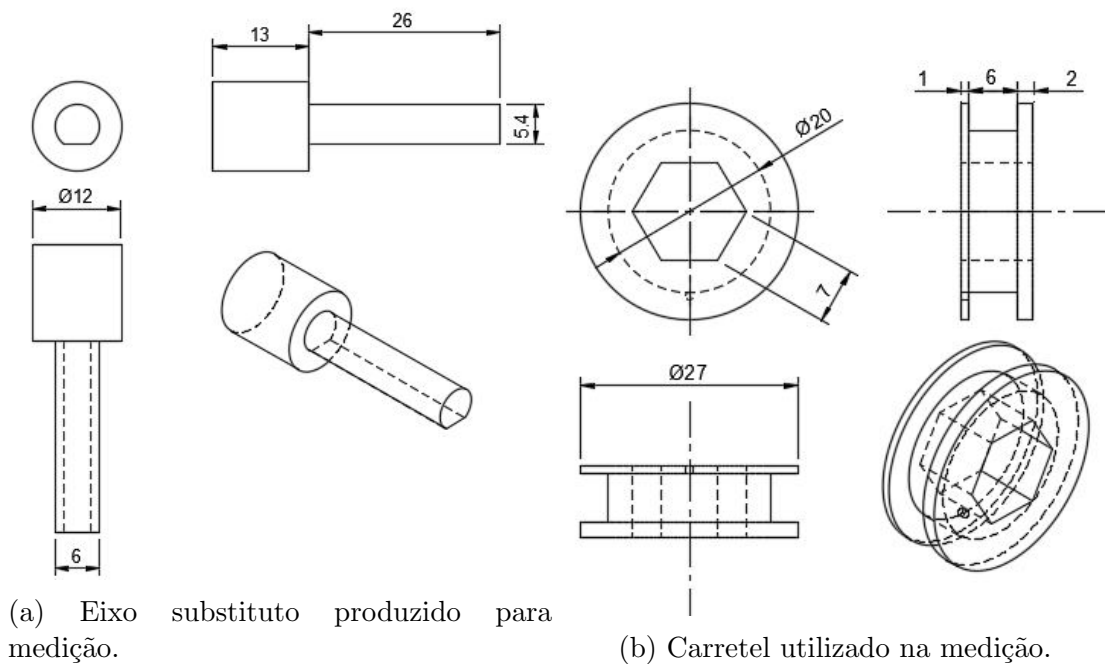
Desenho técnico de fabricação das peças adicionais utilizadas durante o ensaio de esforços de colheita, cotado em mm.
